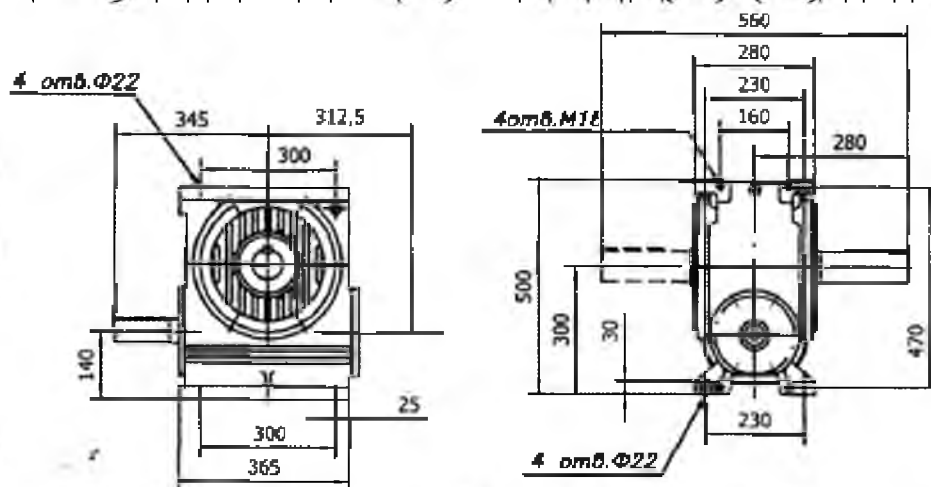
Ескіз черв'ячного редуктора Ч-160
